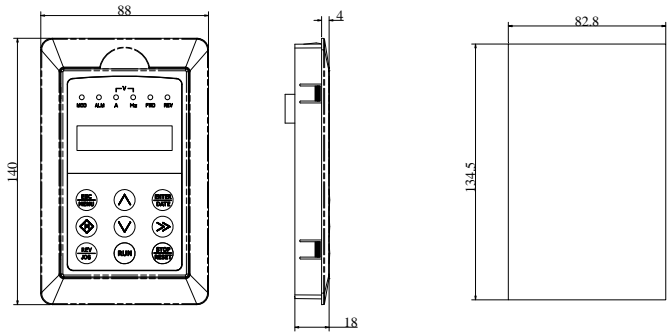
EN-LED1 键盘安装盒外形安装尺寸 图 2-6 键盘安装盒开孔尺寸
